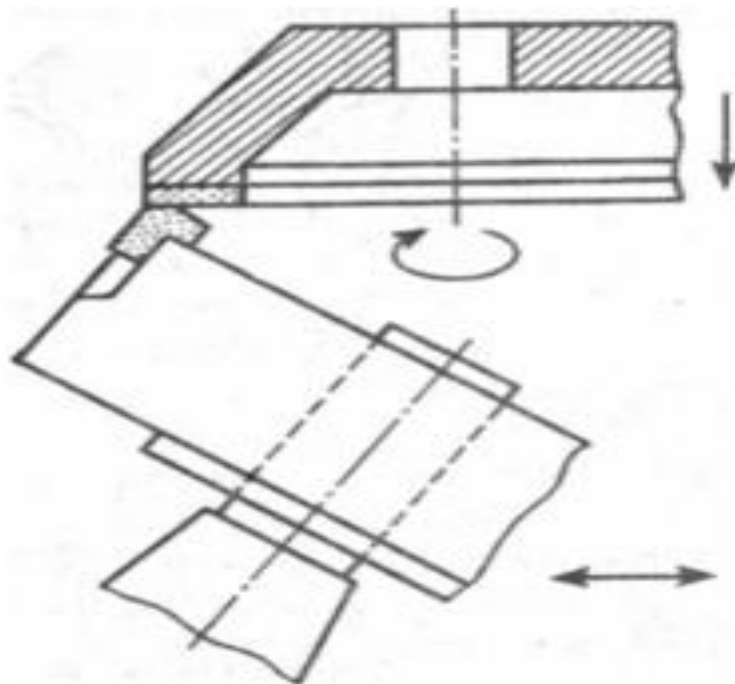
Схема заточки задней поверхности зубьев торцовых фрез.
